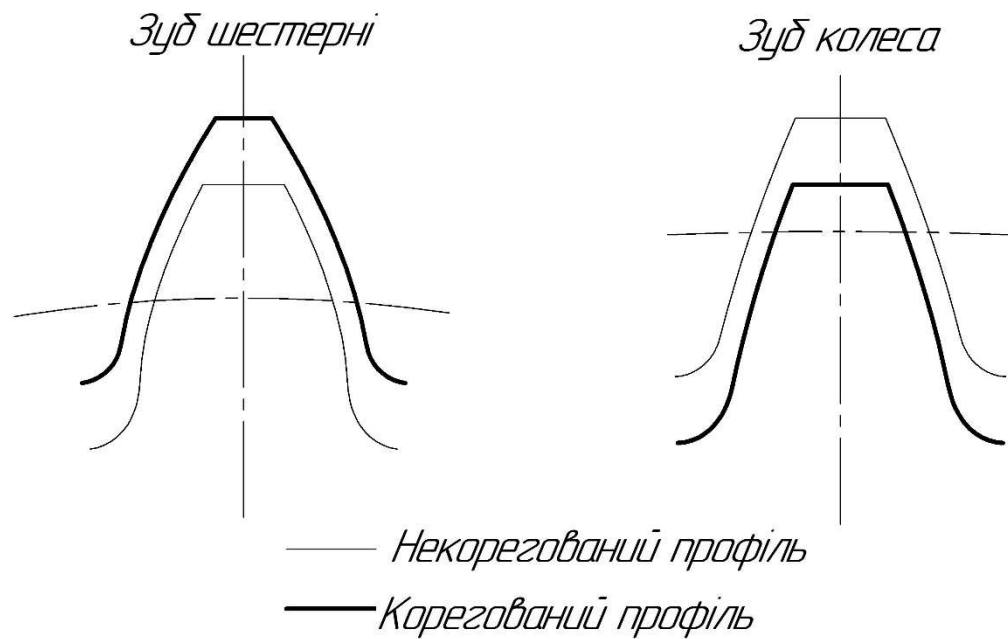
Профілі зубців шестерні і колеса до і після корегування
